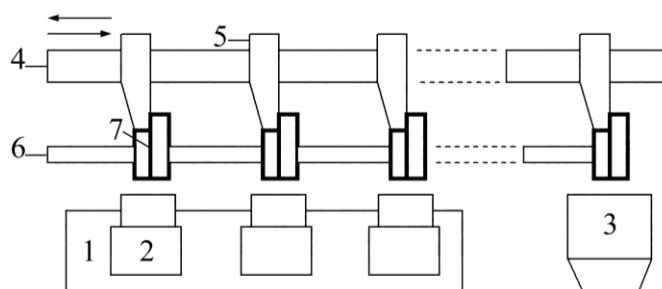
Устройство для ПЭХТО с применением шагового конвейера: 1 – бак-станина; 2 – ванна; 3 – спрейер; 4 – толкающая штанга; 5 – защелка; 6 – направляющий пруток; 7 – обрабатываемая деталь [134].
